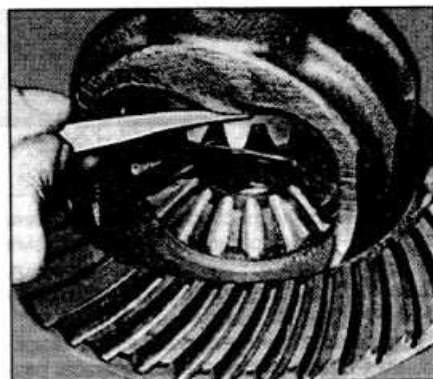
Измерение осевого зазора полуосевой шестерни
